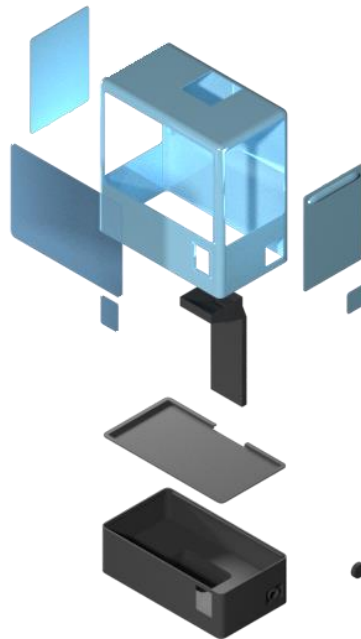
Petunjuk material komponen Disinfection chamber. (Sumber : Dokumentasi Penulis)
